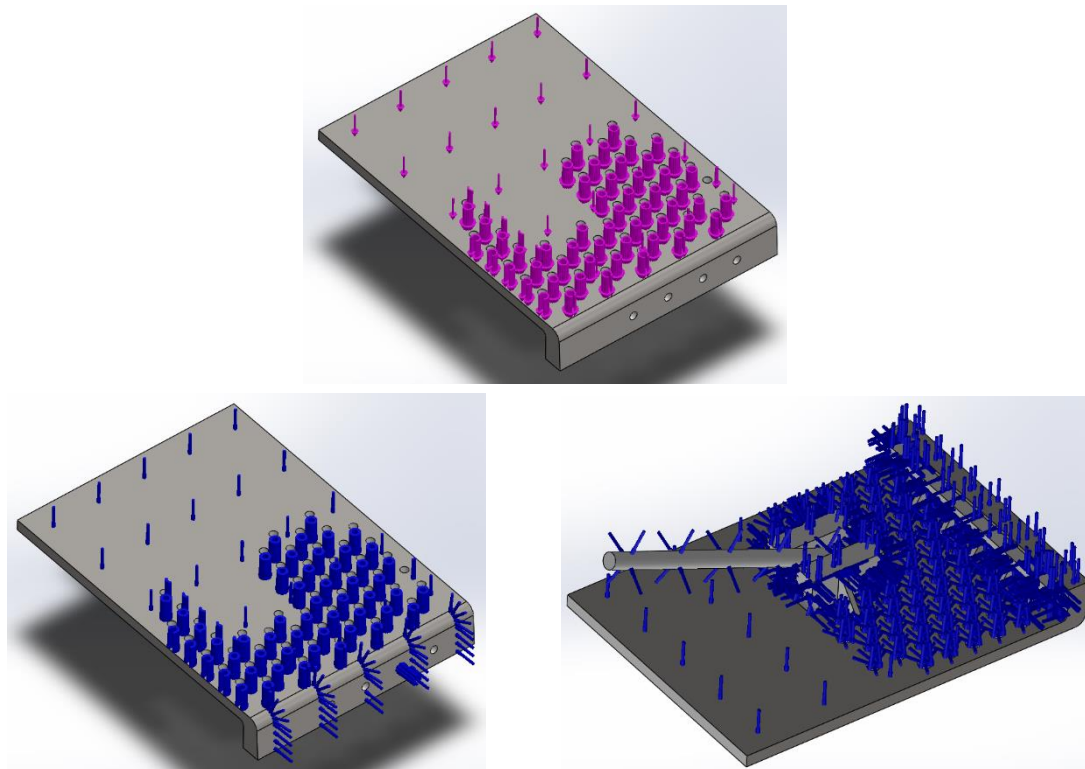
Cargas Aplicadas à Montagem da Placa Proposta
